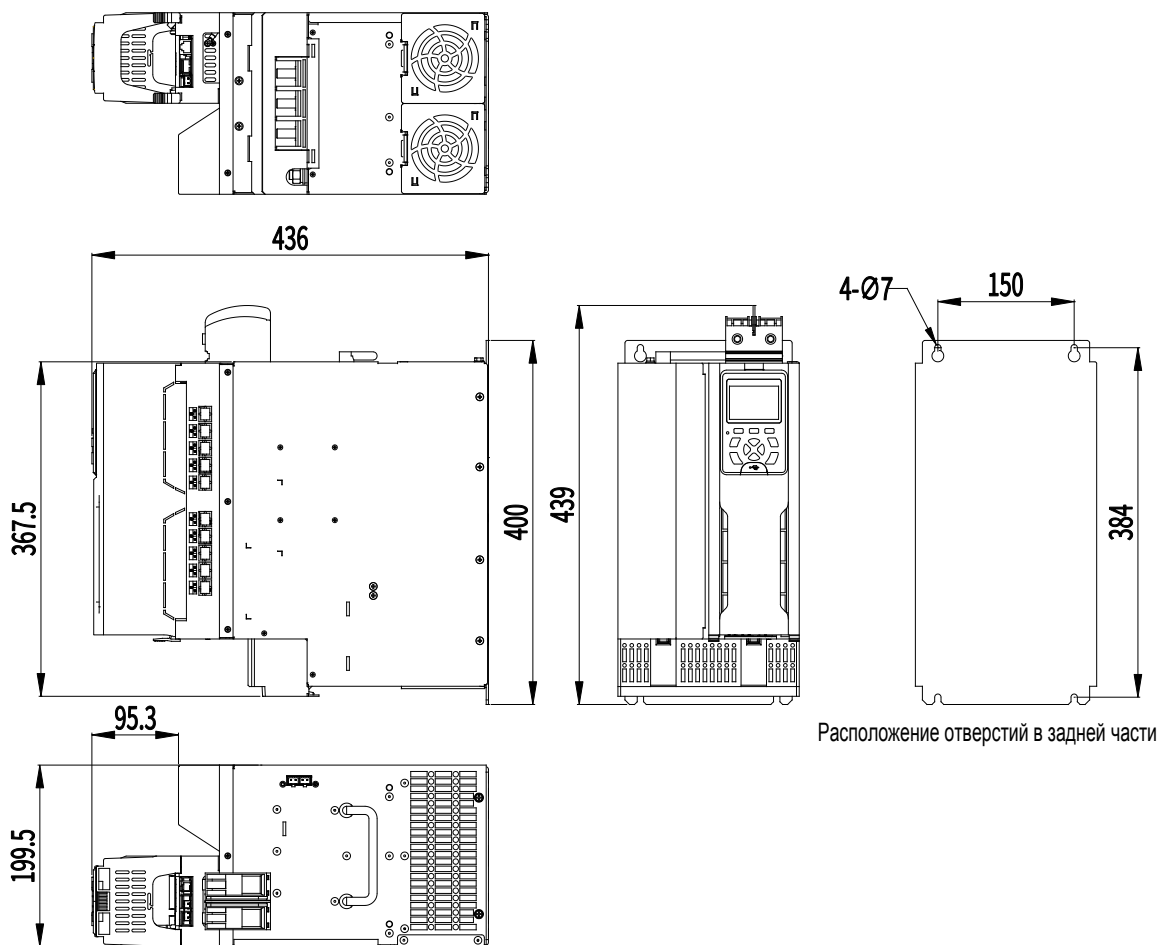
Установочные размеры инверторного блока А6i (единица измерения: мм)
